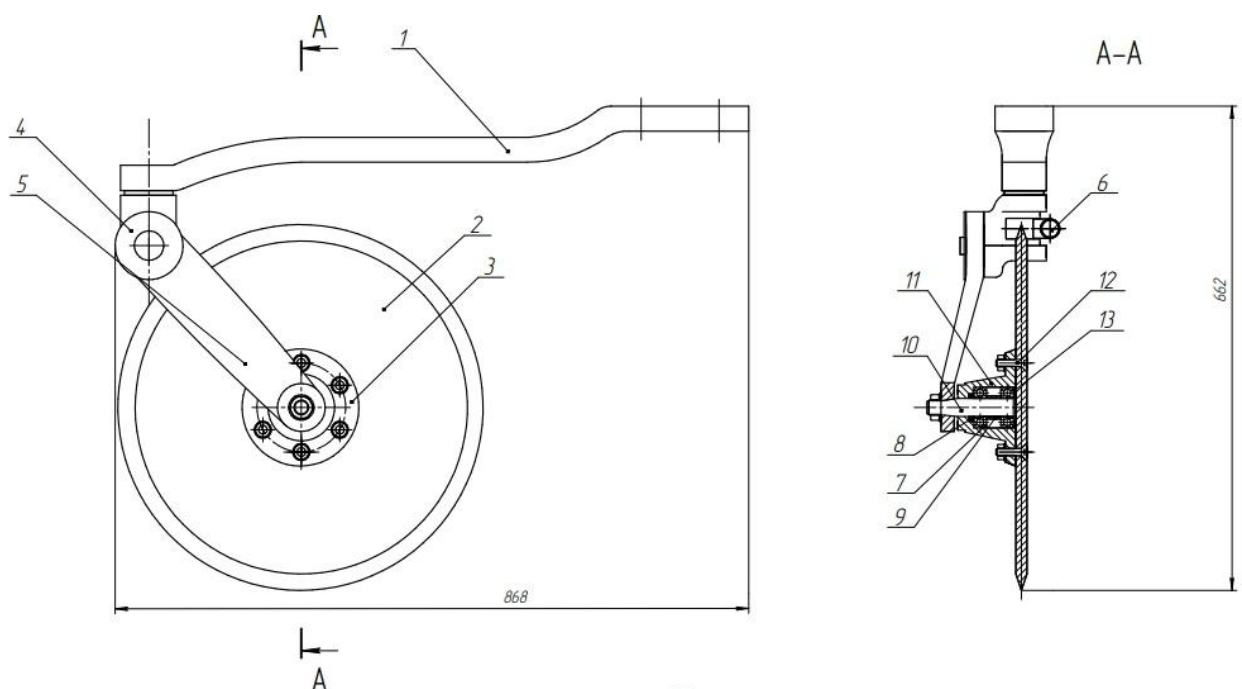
Схема дискового ножа для обладнання оборотного плуга
